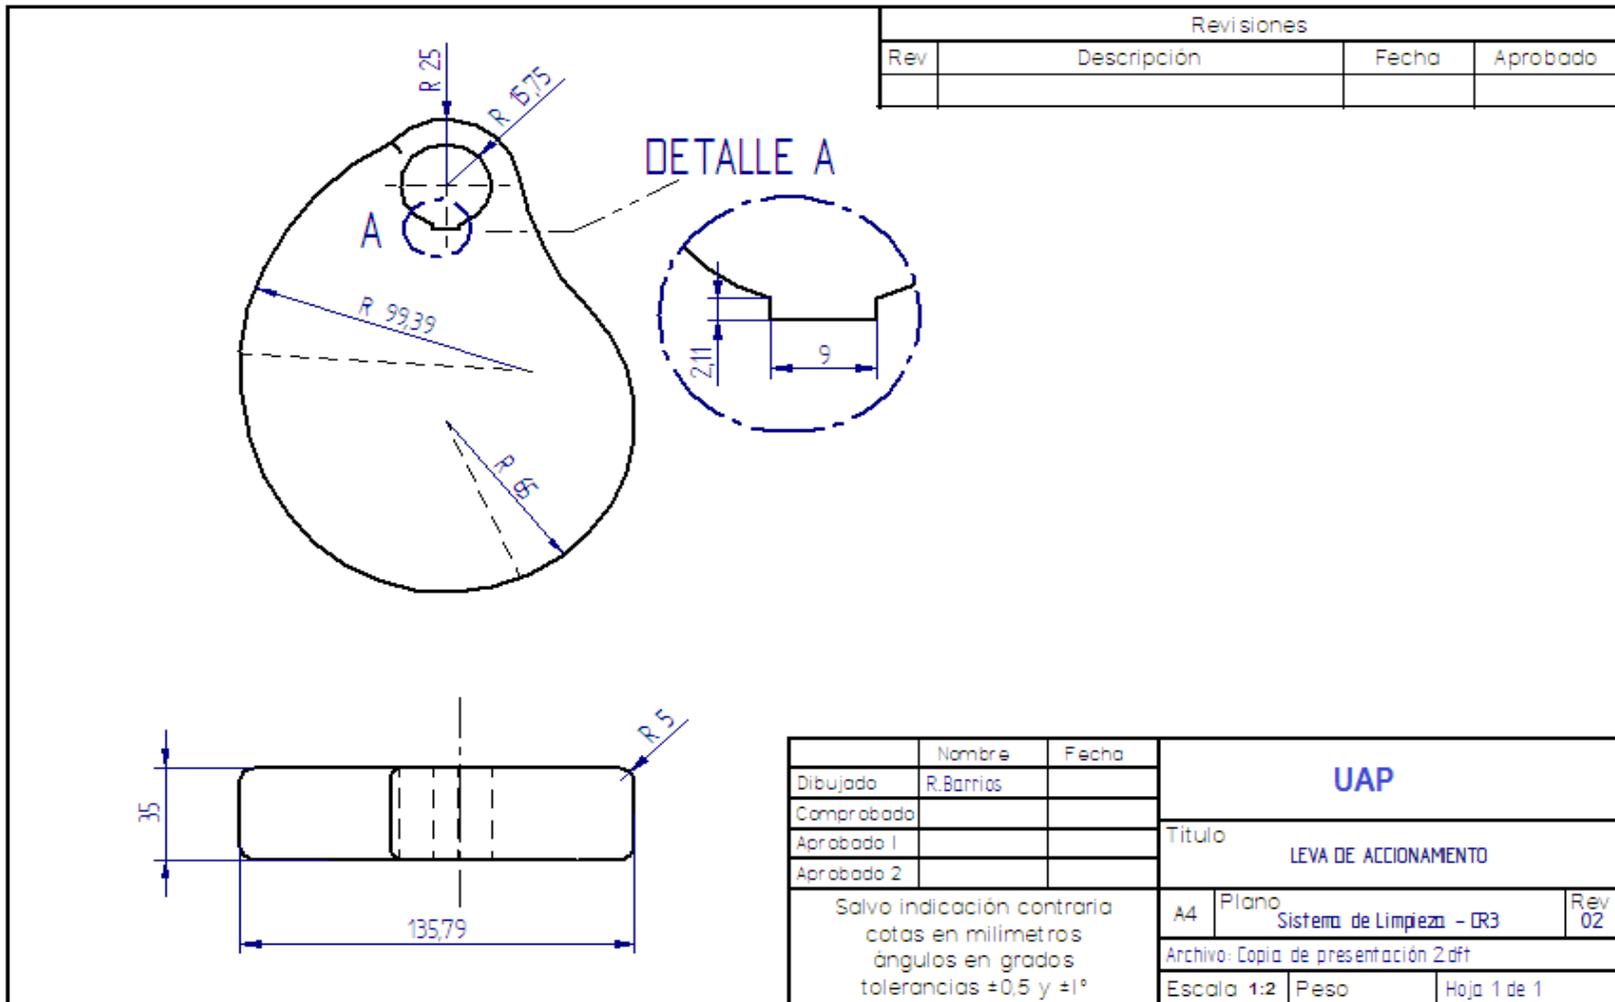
Plano de fabricación para la leva de accionamiento del sistema de limpieza.
